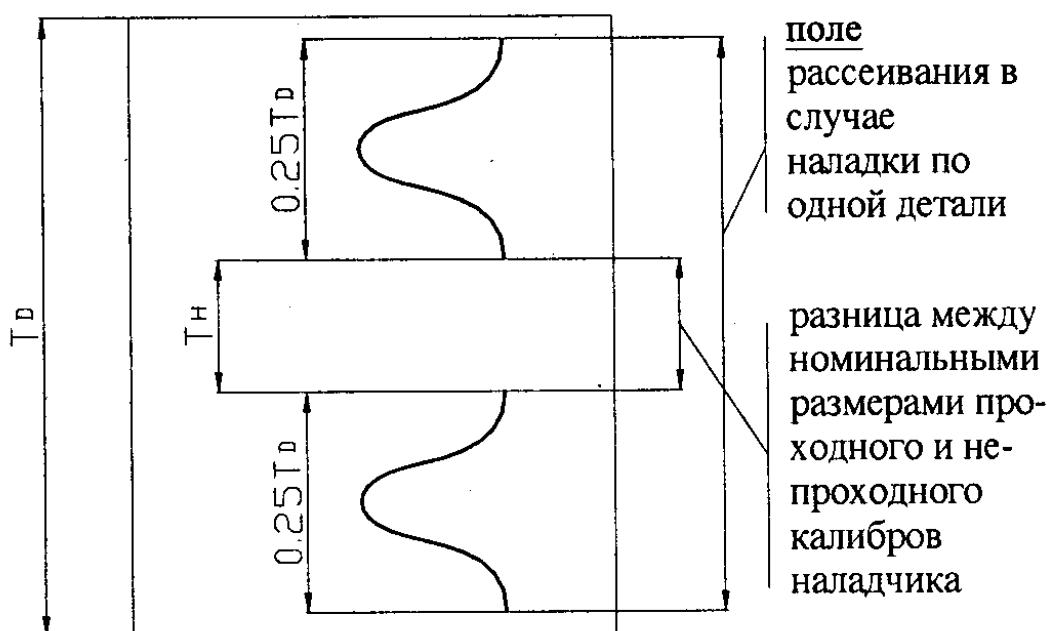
Схема расположения номинальных размеров калибров наладчика в поле допуска детали
